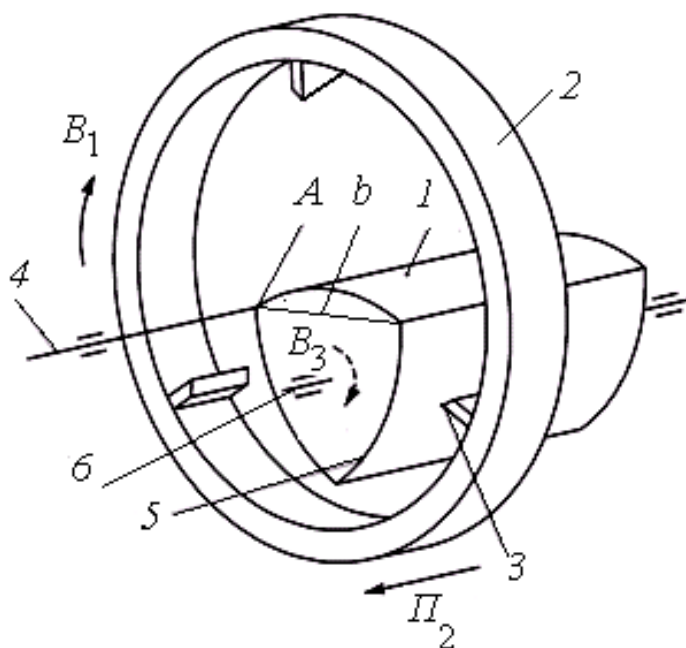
Кинематическая схема кругового точения детали с профилем в виде треугольника Рело охватывающим инструментом
